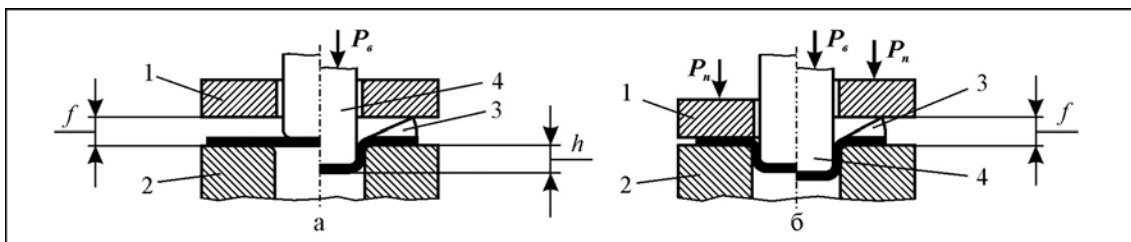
Фази процесу пульсуючого витягування: а – фаза витягування без притиску фланця; б – фаза правлення складок на фланці; 1 – притискне кільце; 2 – матриця; 3 – заготовка; 4 – пуансон
